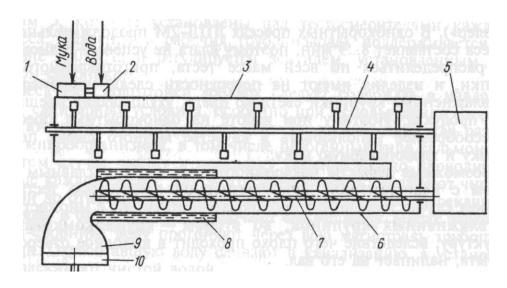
Макаронный пресс: 1 и 2 – дозаторы муки и воды; тестомеситель: 3 – корыта; 4 – вала с лопатками; прессующее устройство: 6 – шнековый цилиндр; 7 – шнек; 8 – водяная рубашка; 9 – прессовая головка; 10 – сменная матрица; 5 - привод
